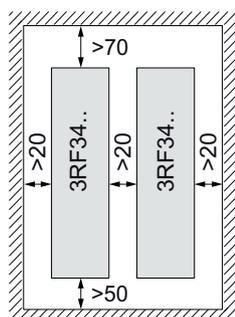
Distancias con instalación independiente (dimensiones en mm)
